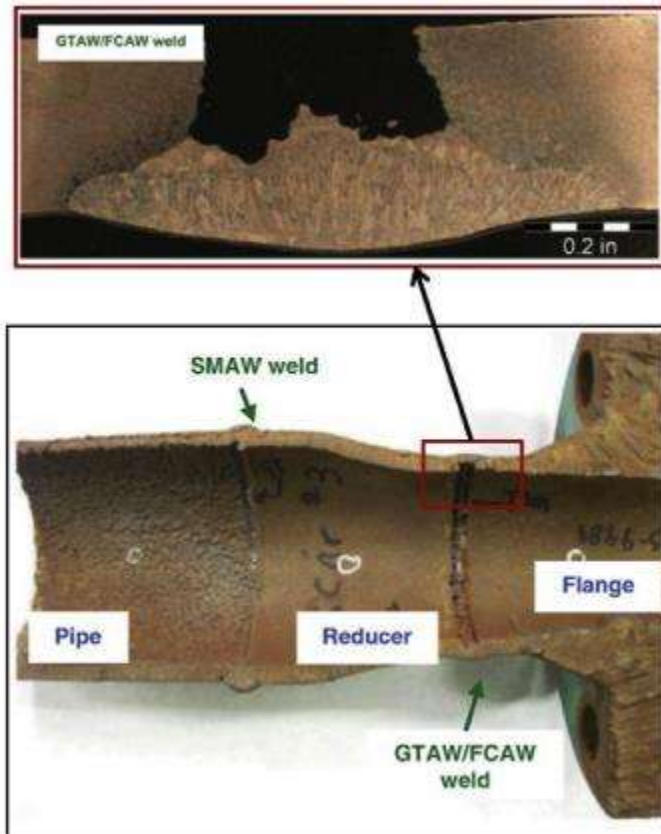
9 Soldadura corroída en una sección de línea de flujo [12]
